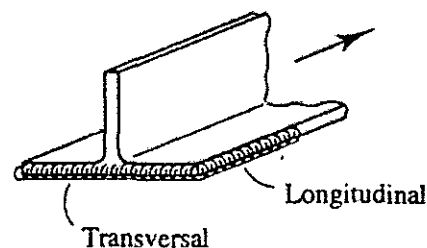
Soldadura Longitudinal y transversal
